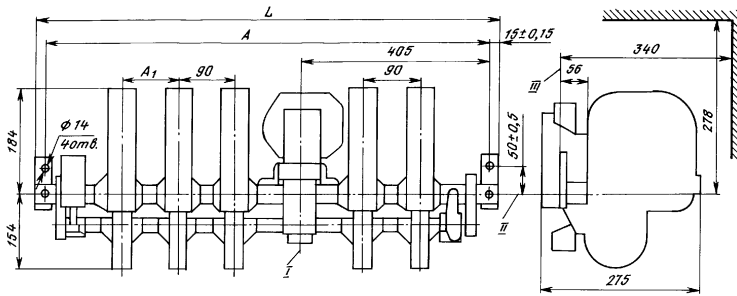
Габаритные и установочные размеры контакторов КТ6044 и КТ6045
